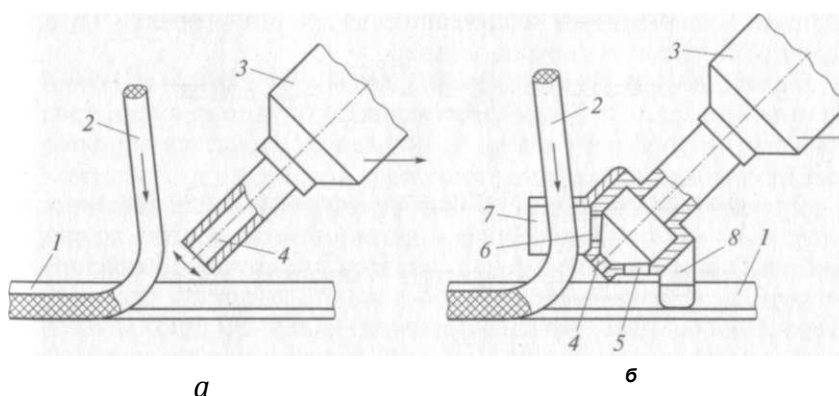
Схема ручной газовой прутковой (а) и скоростной (б) сварки:
